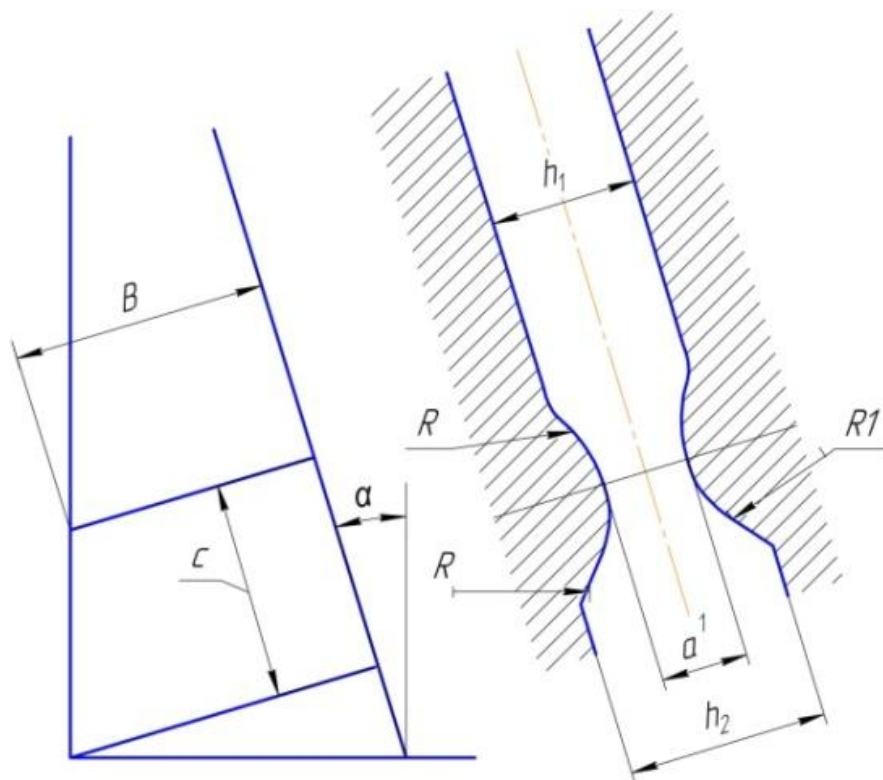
Протяжной ручей открытого типа, расположенный под углом α к оси штампа
